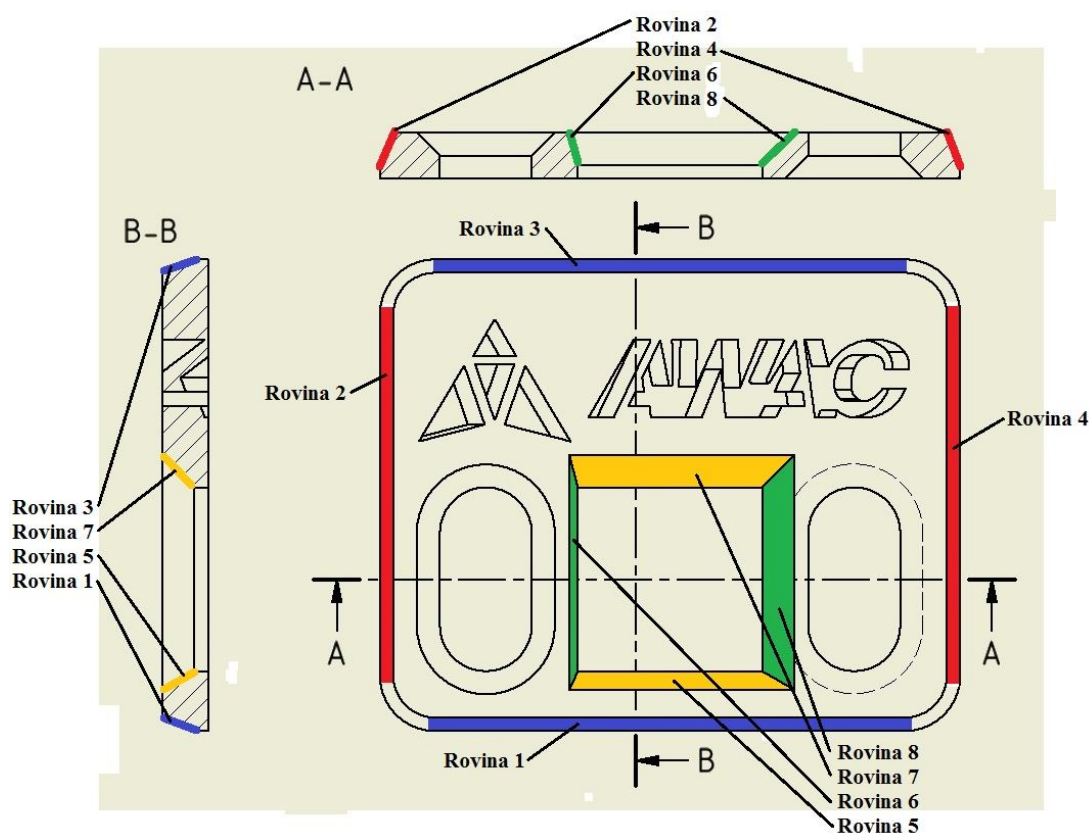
Zakótované měřené rozměry vzorku obdélník AWAC.
